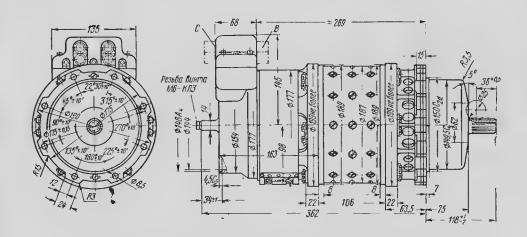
Габаритные размеры стартер-генератора СТГ-12ТМО-1000
